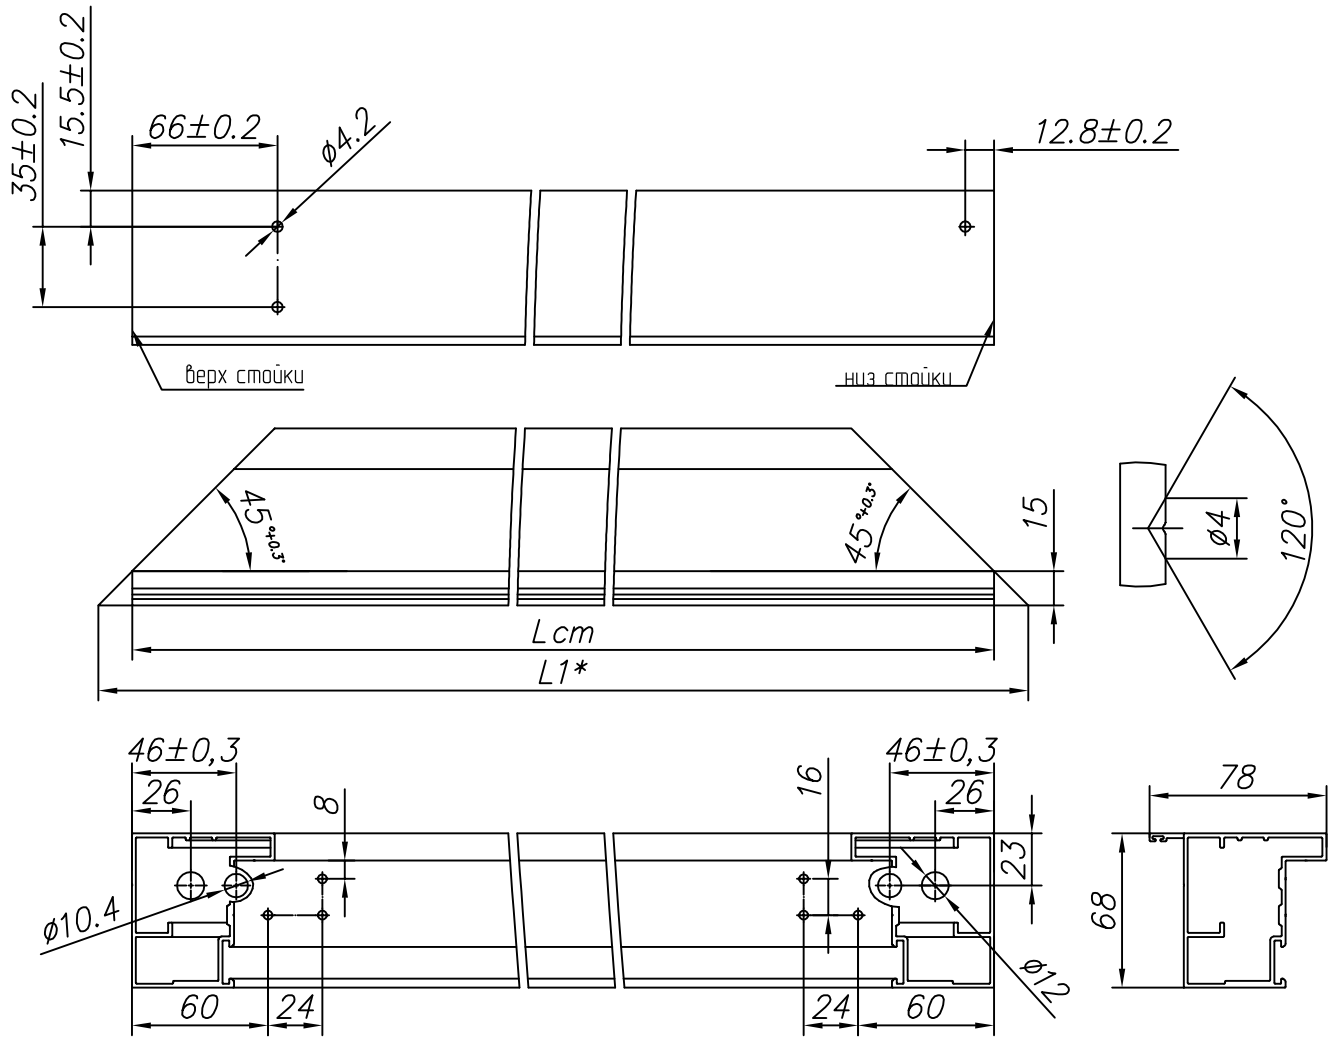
Изготовление стойки из профиля FLGU.400.0108 (стойка левая, открывание калитки наружу)
